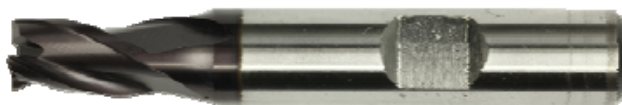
Langlochfräser (Bohrnutenfräser) von GÜHRING für die Bearbeitung von Titanlegierungen. Ausführung: Typ N, DIN 327, 30°, ab Ø 3,0 mm mit Zentrumschnitt. HSS Co8, Fire-beschichtet. Der Fräser hat 3 Zähne. (Beschreibung aus: Katalog Premium Werkzeug Handel).
